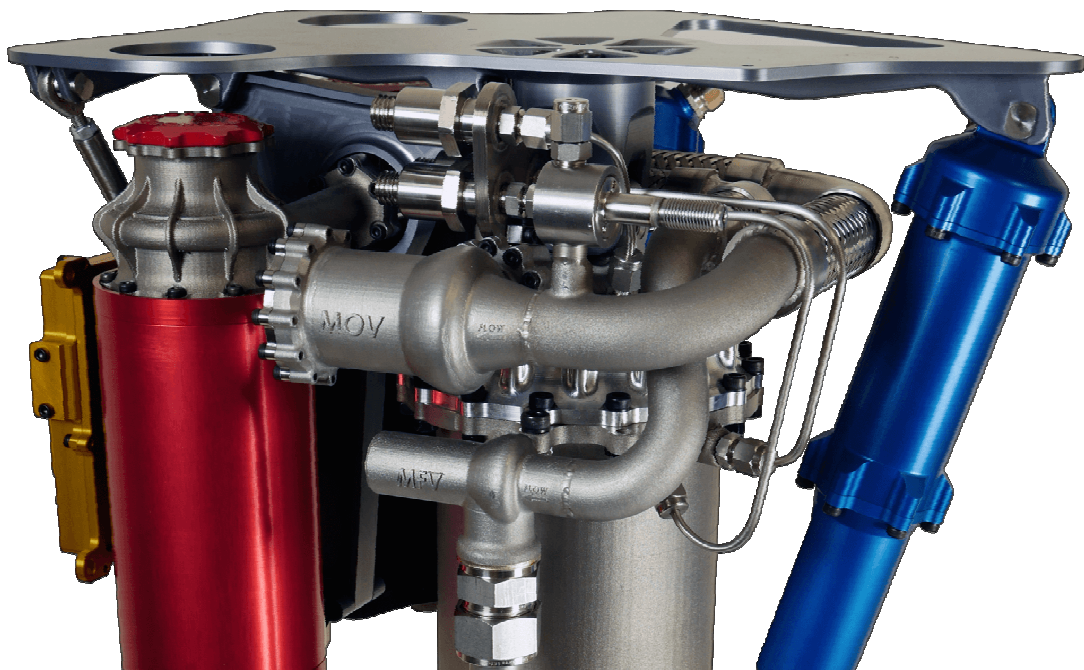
Компонировка агрегатов подачи и управления двигателем Rutherford.
